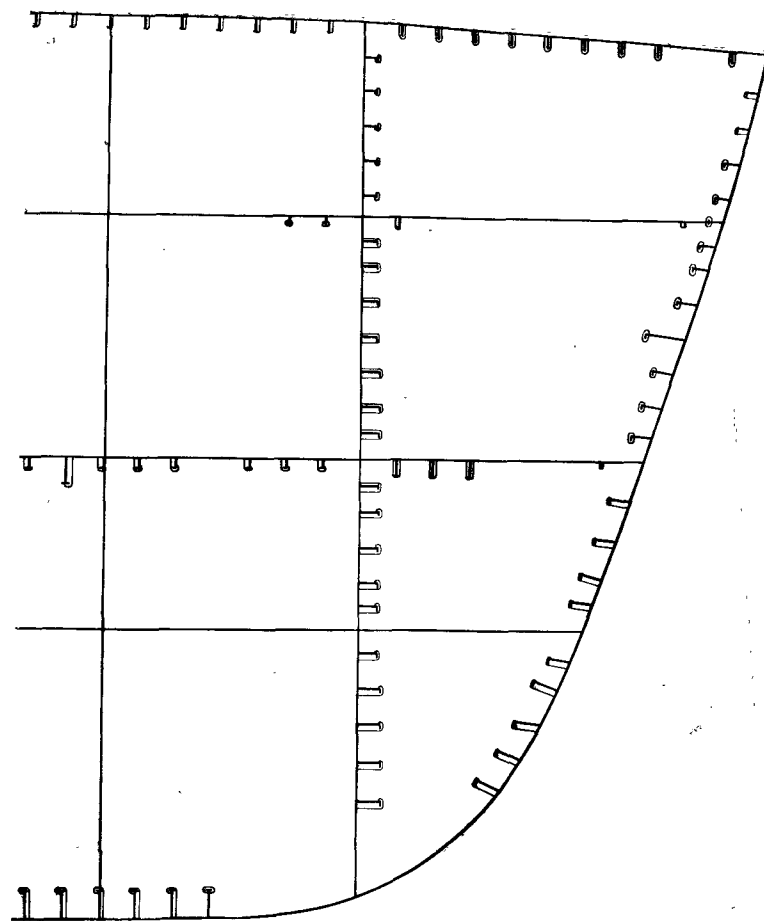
Конструктивный чертеж поперечного сечения корпуса, полученный с помощью подсистемы PRIMARY (праймэри).
